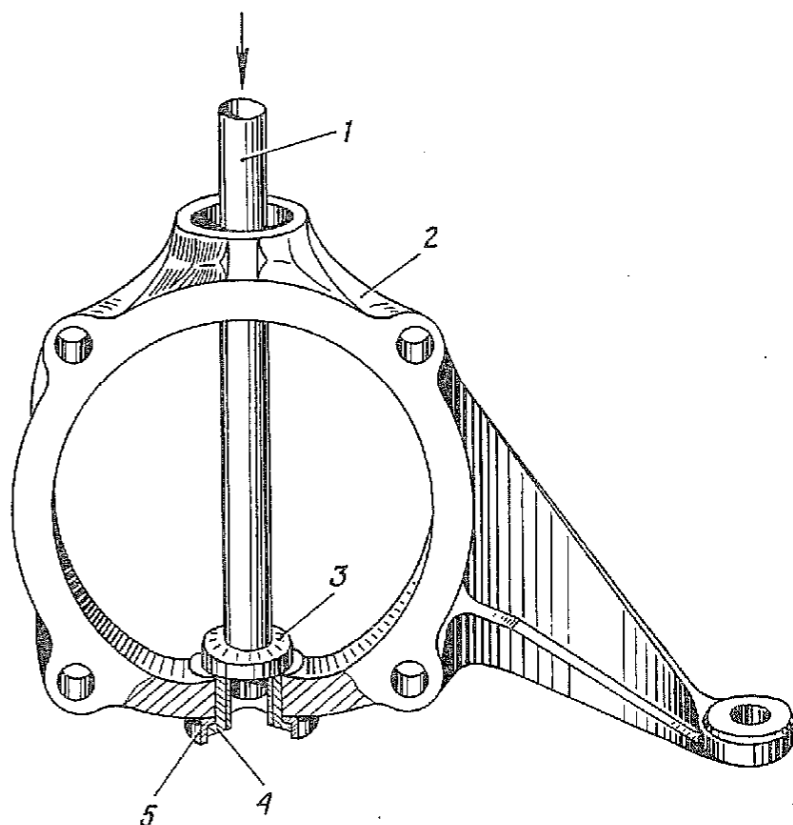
Выпрессовка корпуса втулки шкворня с втулкой в сборе:
